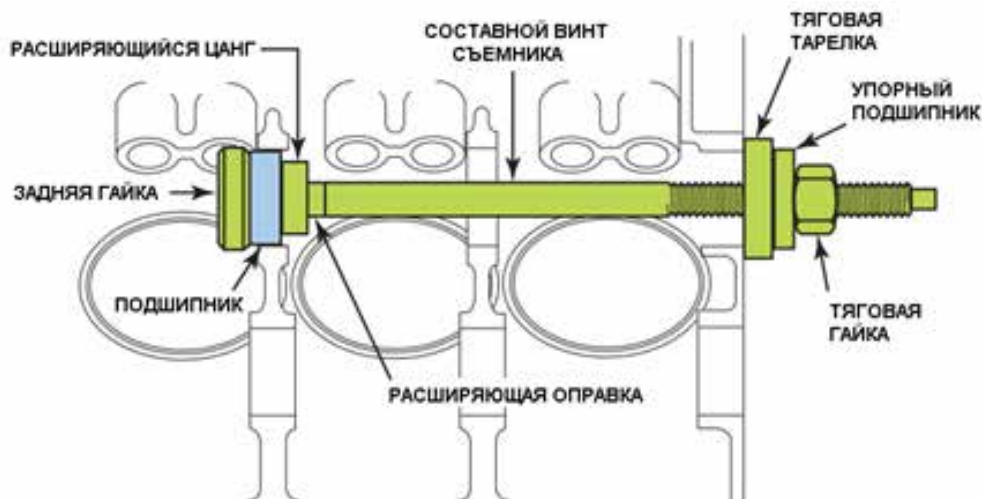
Винтовой съемник используется для установки новых подшипников распределительного вала. Большинство подшипников кулачкового вала неразрезного типа устанавливаются в отверстия блока цилиндров или головки цилиндров прессовой посадкой. Производитель автомобильных двигателей рекомендуют производить посадку подшипника без использования смазок, чтобы предотвратить их проворачивание в гнезде, и блокирование подачи смазки; источник: *Pearson Education, Inc.
